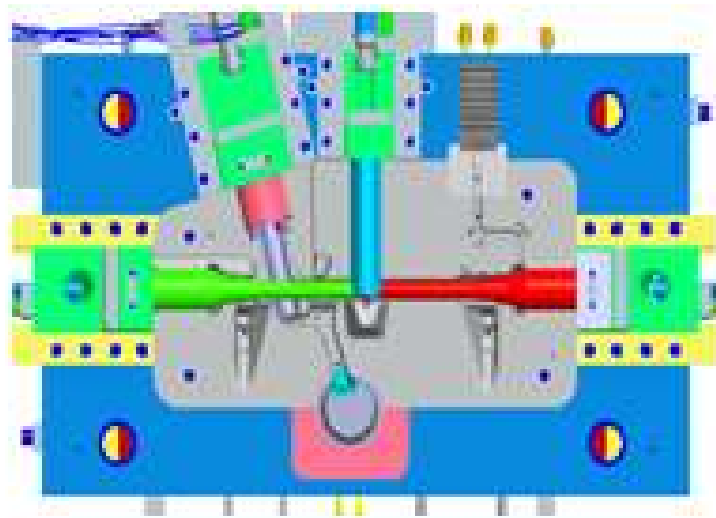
Interior molde parte móvil y pieza antes de pasar por la matriz o troquel
